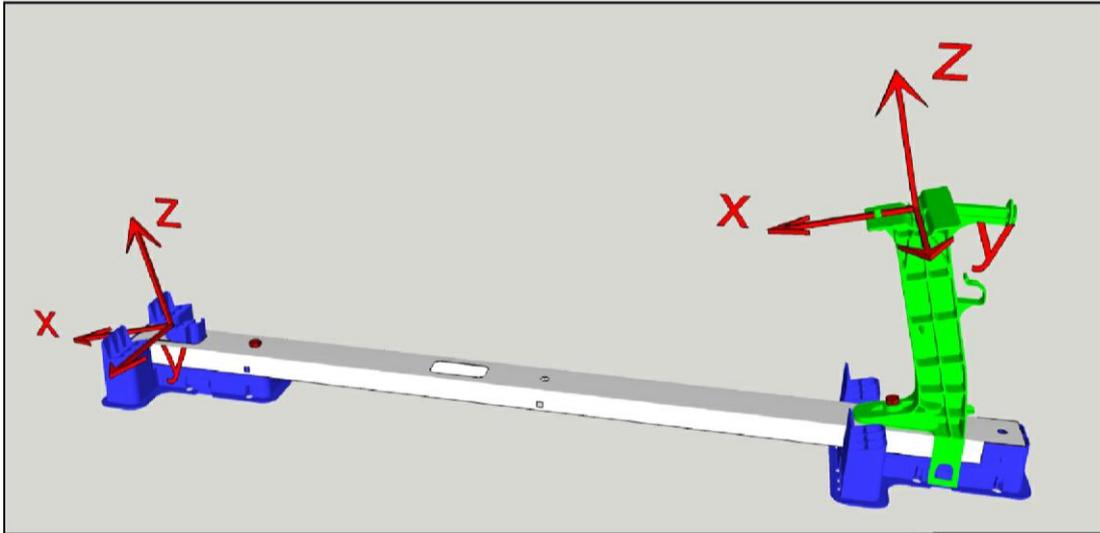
Unterkonstruktion Stützen-Fuß-Modul mit Stahlprofil
